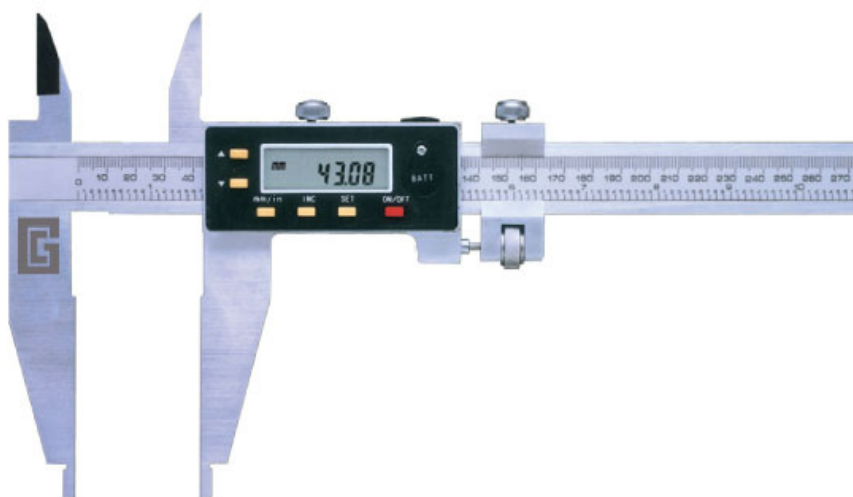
Общий вид штангенциркулей типа ШЦЦ-V.
